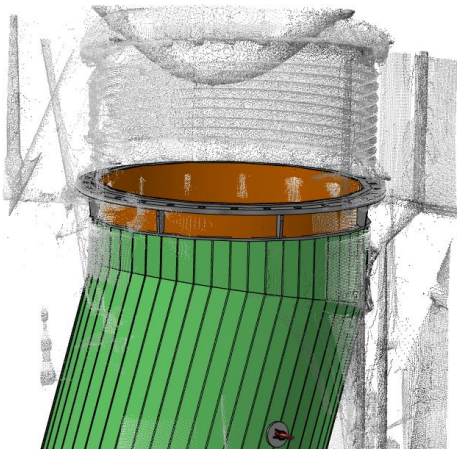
Anschlußpunkt mit Flanschkontrolle für ein Gasausgleichsrohr; Flanschdurchmesser 1.200mm
